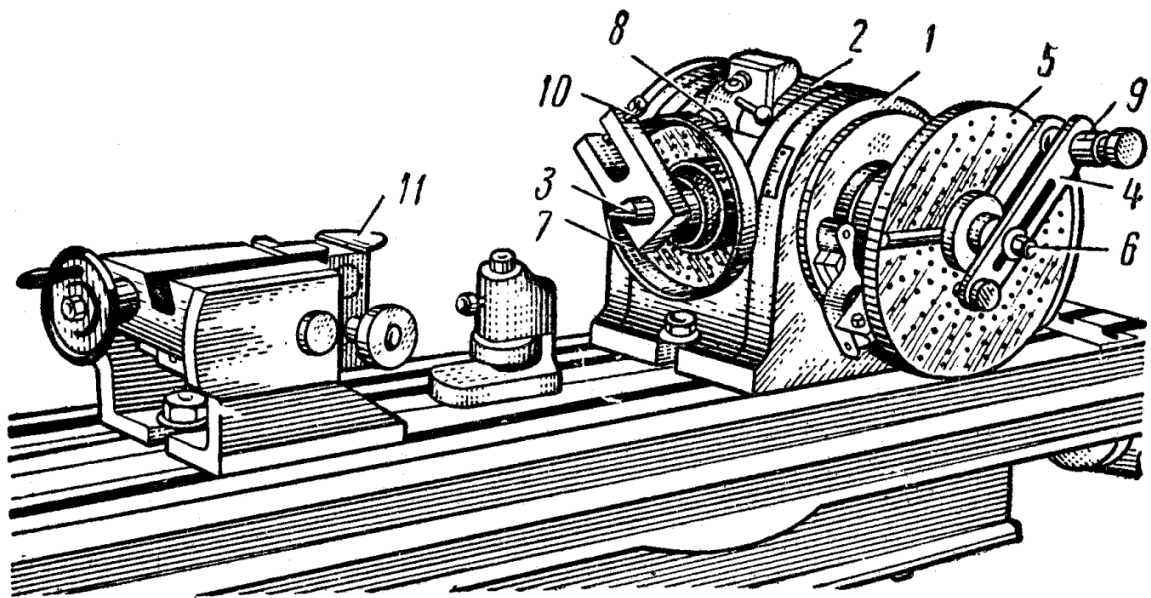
Общий вид универсальной делительной головки УДГ-100: 1- корпус, 2- поворотная часть, 3 – шпиндель, 4 – рукоятка, 5 – делительный диск, 6 – валик, 7- диск непосредственного деления, 8,9 – штифты, 10 – поводок, 11 – задняя бабка
